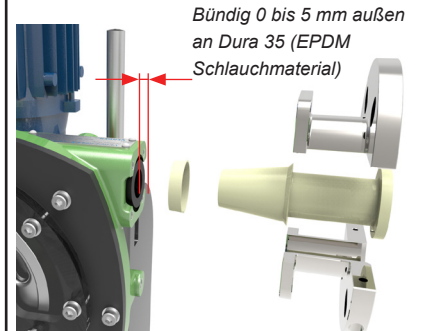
Schlauch bündig (geteilter Flansch)
